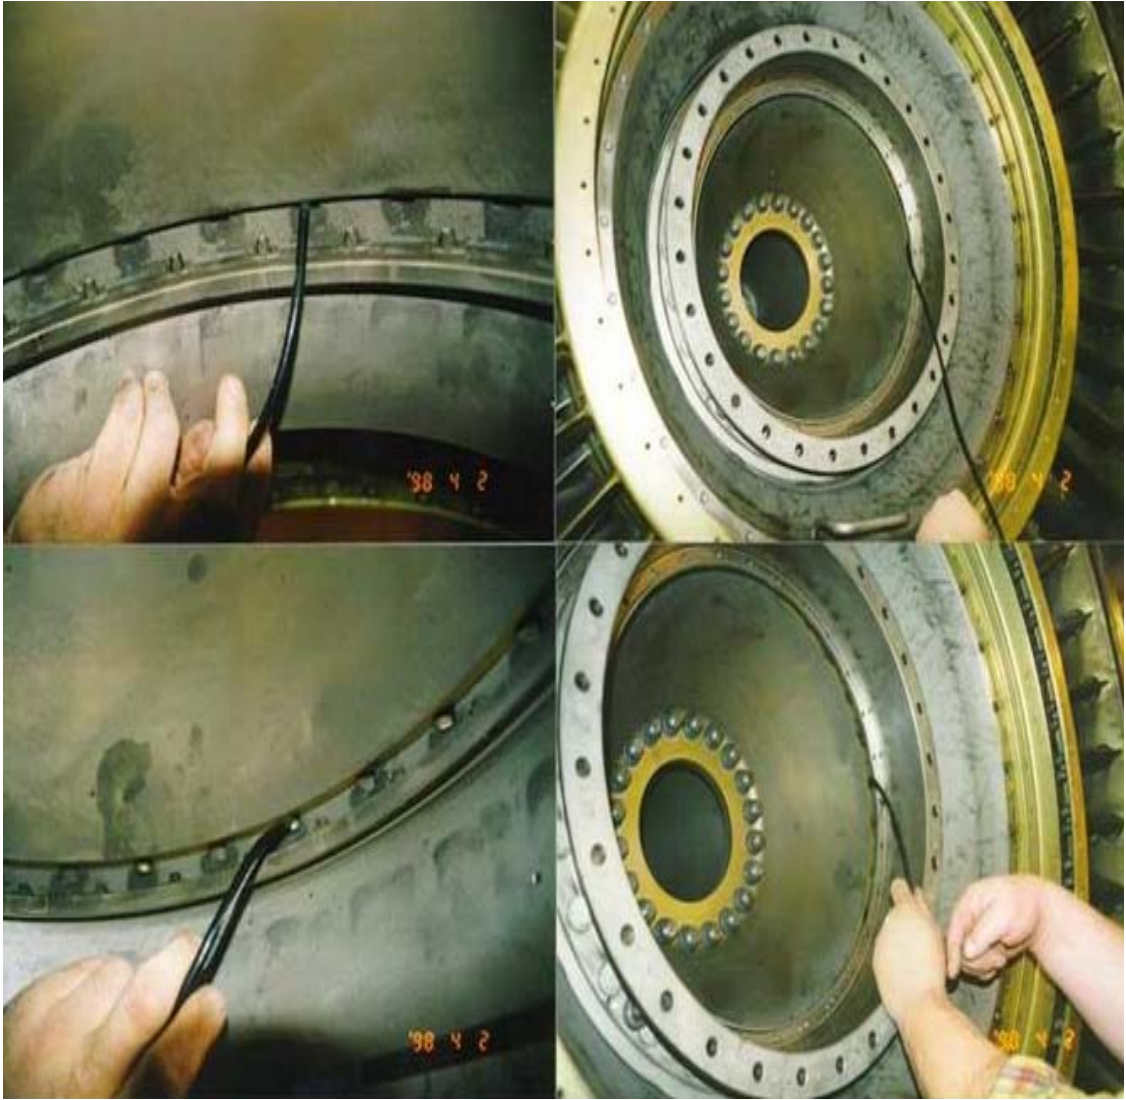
INSPECCIÓN FÍSICA DE UNA PARTE DEL COMBUSTOR
